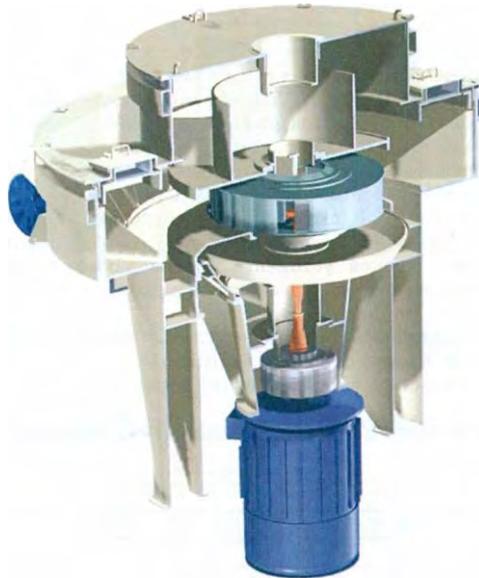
Внешний вид центробежно-ударной машины для дробления типа ДЦ-1,25⁶¹
